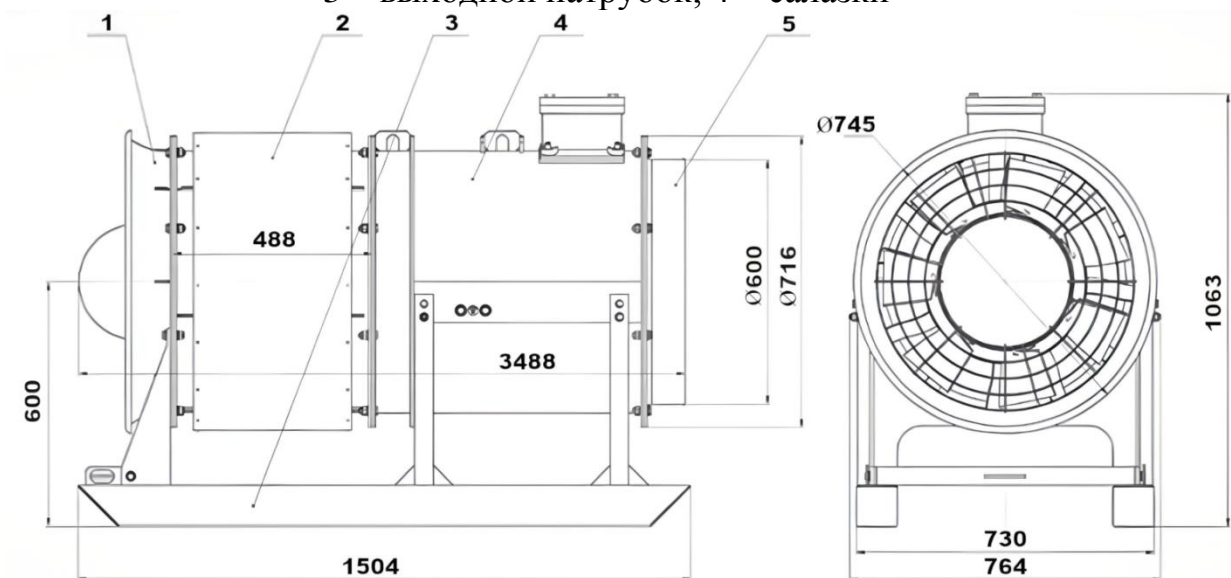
Вентилятор ВМЭ-6М/1 с глушителем шума: 1 – коллектор с коком и предохранительной решеткой; 2 – глушитель шума; 3 – салазки; 4 – вентилятор с двигателем и рабочим колесом; 5 – выходной патрубок
